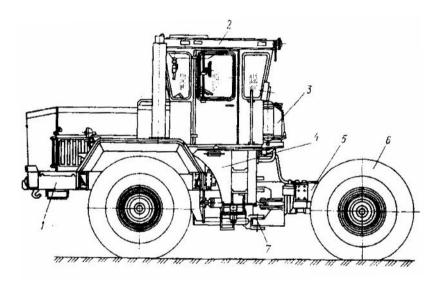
Трактор «Кировец» К-703 М: 1 – передняя полурама; 2 – кабина; 3 – масляный бак; 4 – топливный бак; 5 – задняя полурама; 6 – шина; 7 – универсальный шарнир
